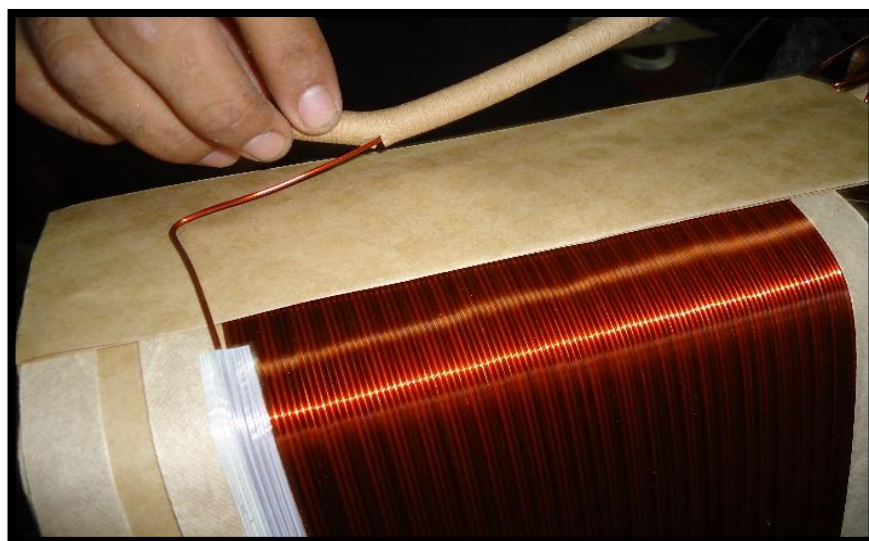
COLOCACIÓN DEL AISLAMIENTO EN EL TERMINAL DEL DEVANADO DE BAJA TENSIÓN.
